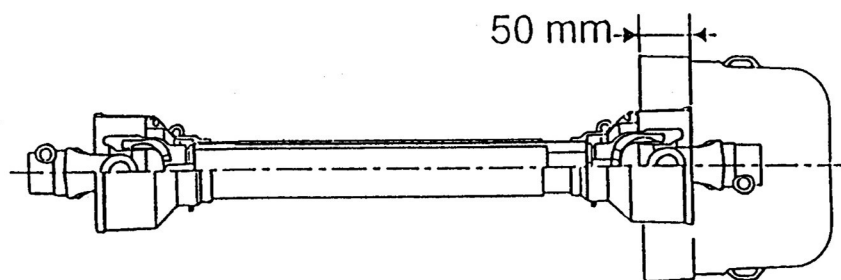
Maschinenseitige Schutzabdeckung
